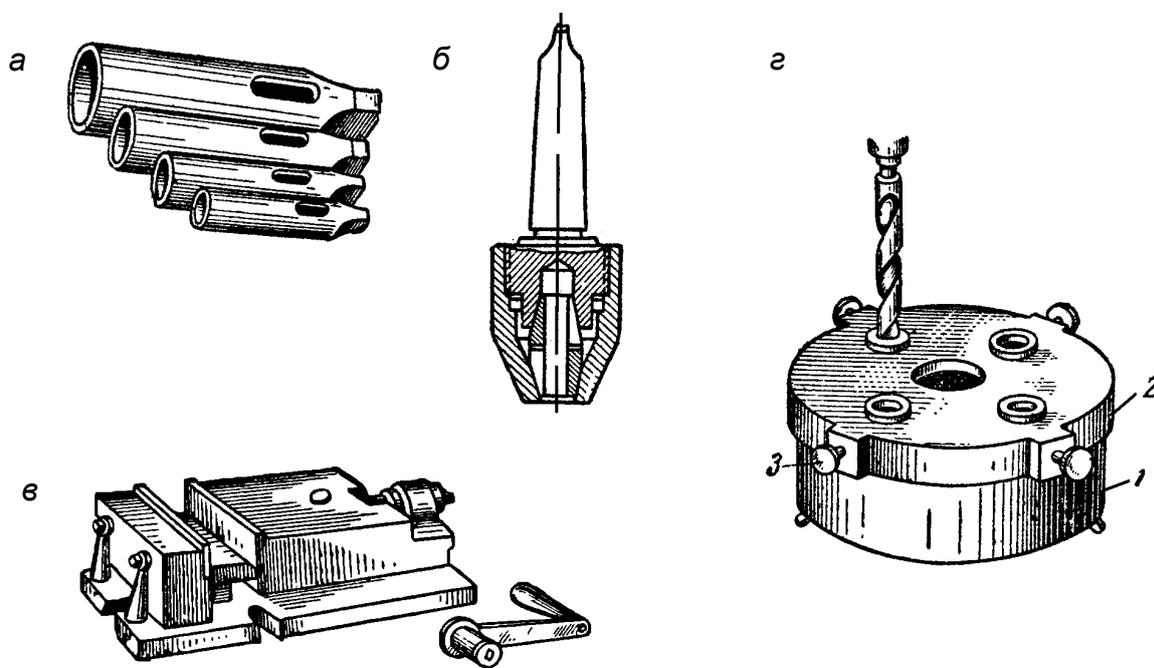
Принадлежности и приспособления к сверлильным станкам: а – переходные конусные втулки; б – патрон для закрепления сверл с цилиндрическими хвостовиками; в – машинные тиски; г – накладной кондуктор; 1 – обрабатываемая деталь; 2 – кондуктор; 3 – винт
